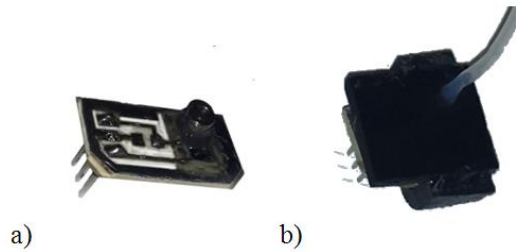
a) PCB con sensor de presión encapsulado b) Ensamble de la tubería con el PCB
